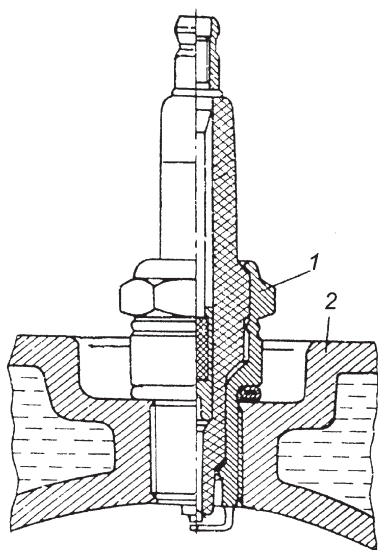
Установка свечи зажигания в головке блока цилиндров:
